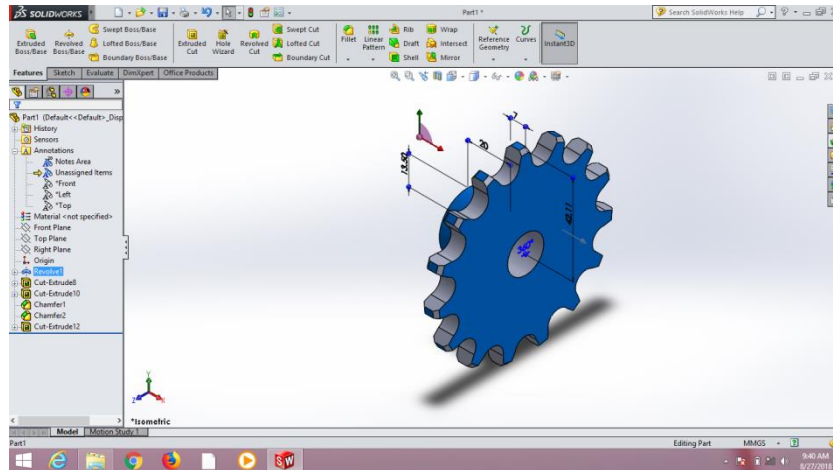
Gambar awal 3 dimensi sprocket kecil
